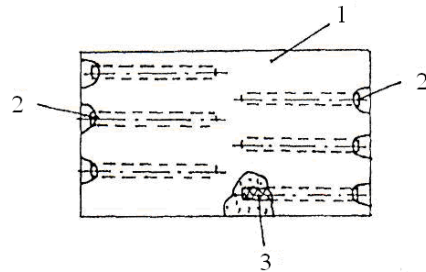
Блок покрытия корпуса кабины [20]:
